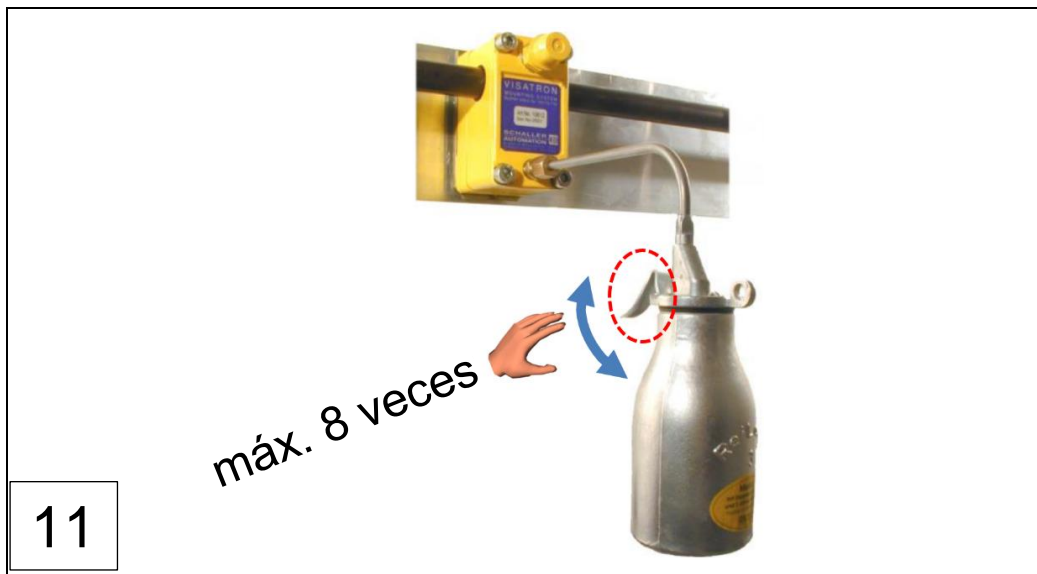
Montaje del módulo de bloque sifónico con puesta en servicio (pasos de montaje 1-11)
